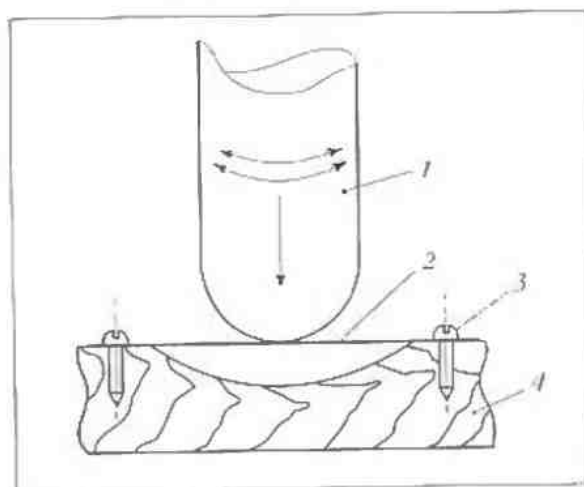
Изготовление чашечки: 1 – округлая палочка “пуансон” (рукоятка стамески); 2 – фольга; 3 – шурупы; 4 – матрица
